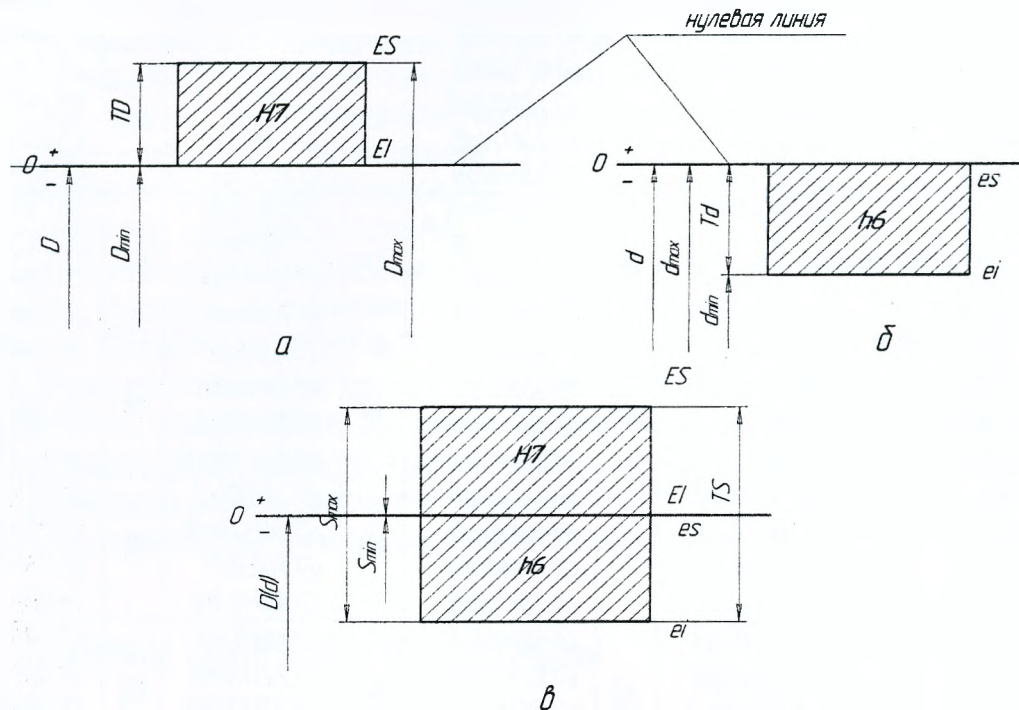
Схемы полей допусков а – отверстия; б – вала; в – посадки
